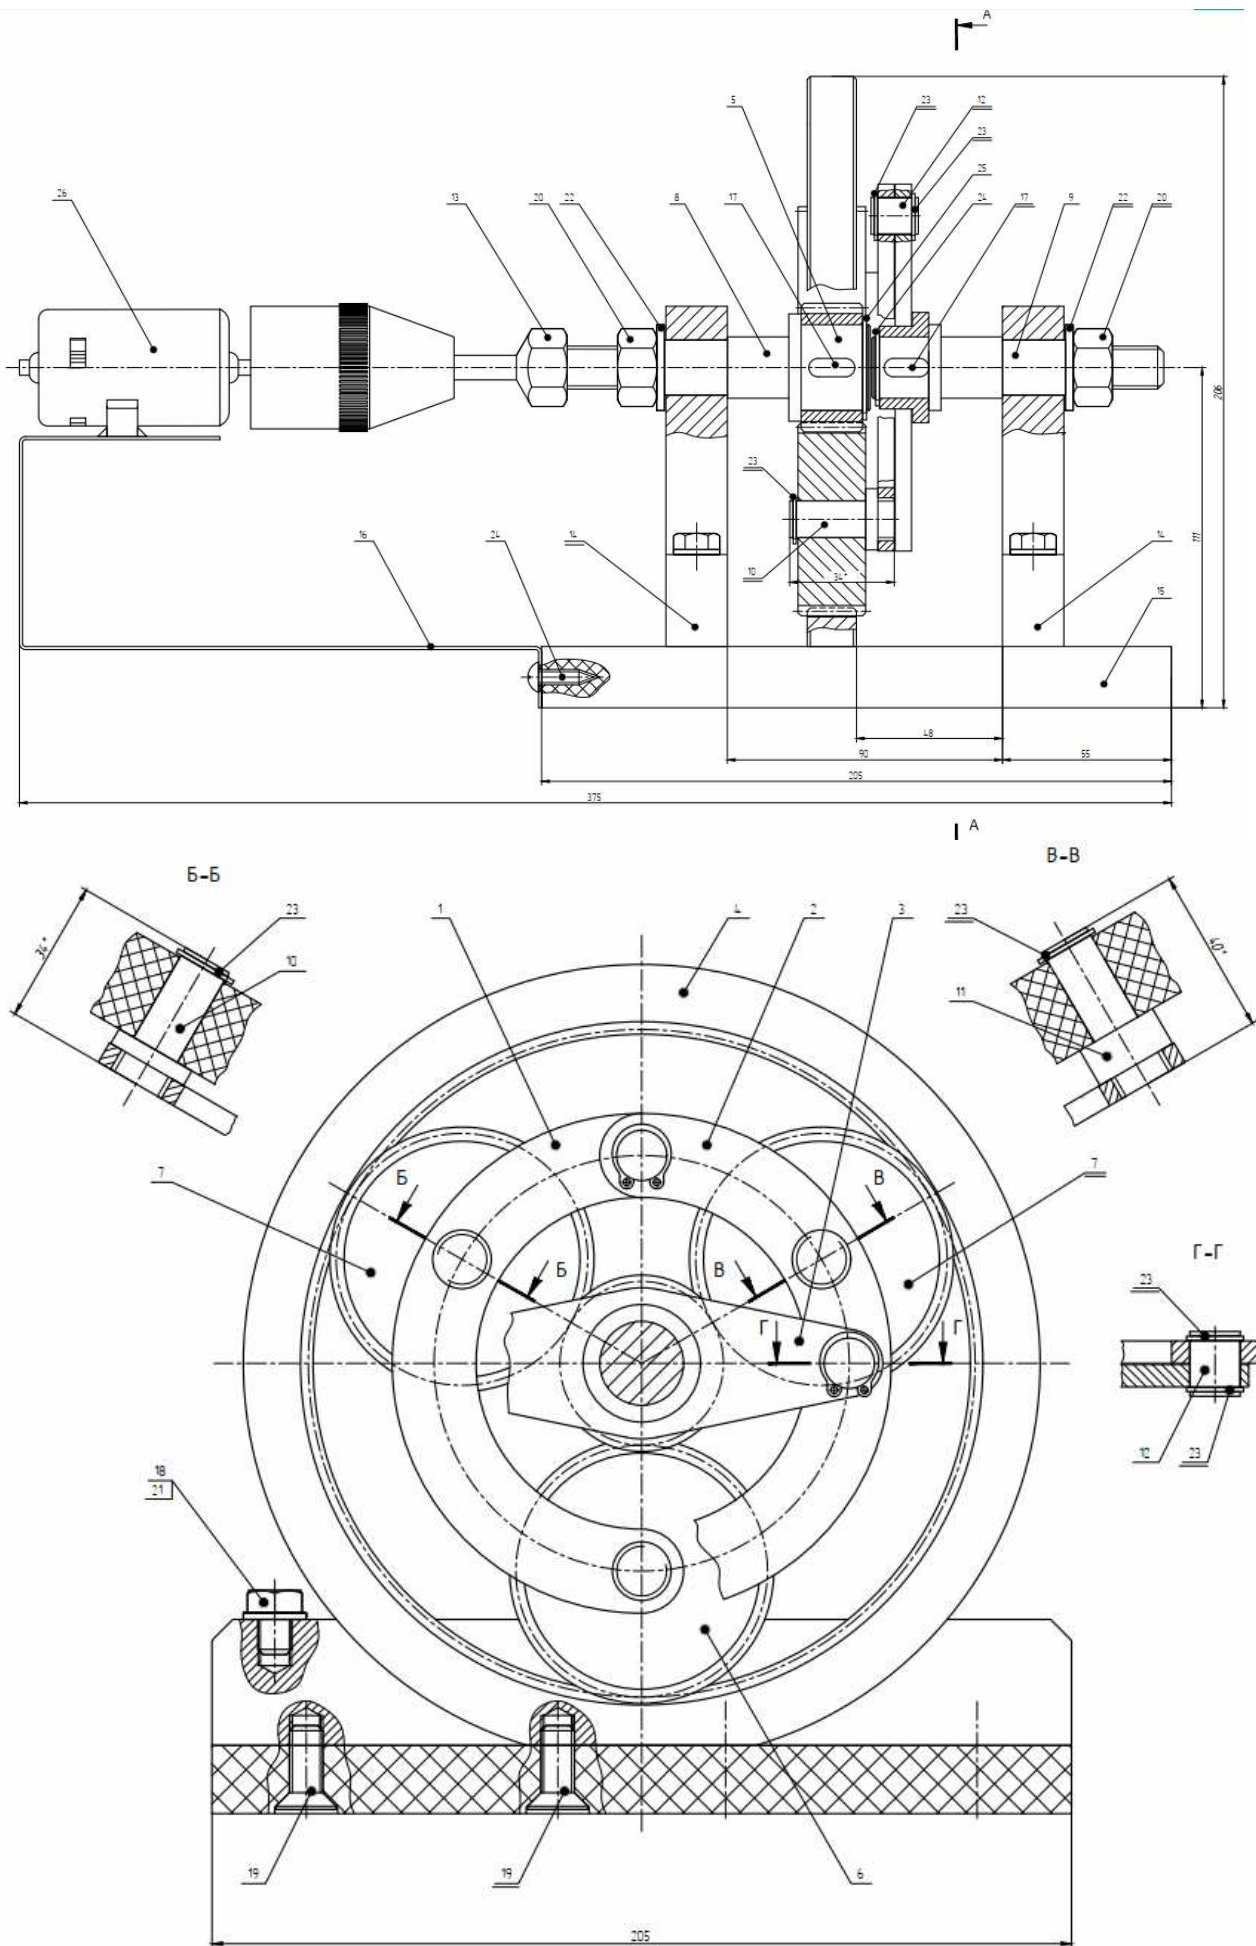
Схематичное изображение стэнда планетарного редуктора
